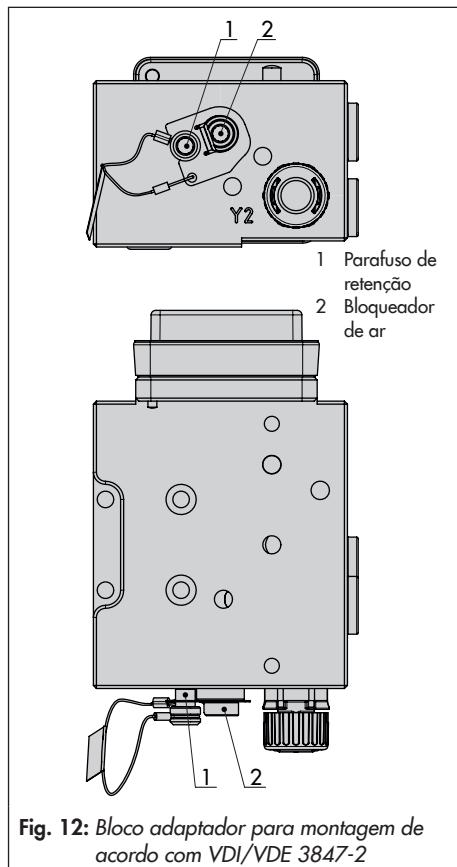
Bloco adaptador para montagem de acordo com VDI/VDE 3847-2
